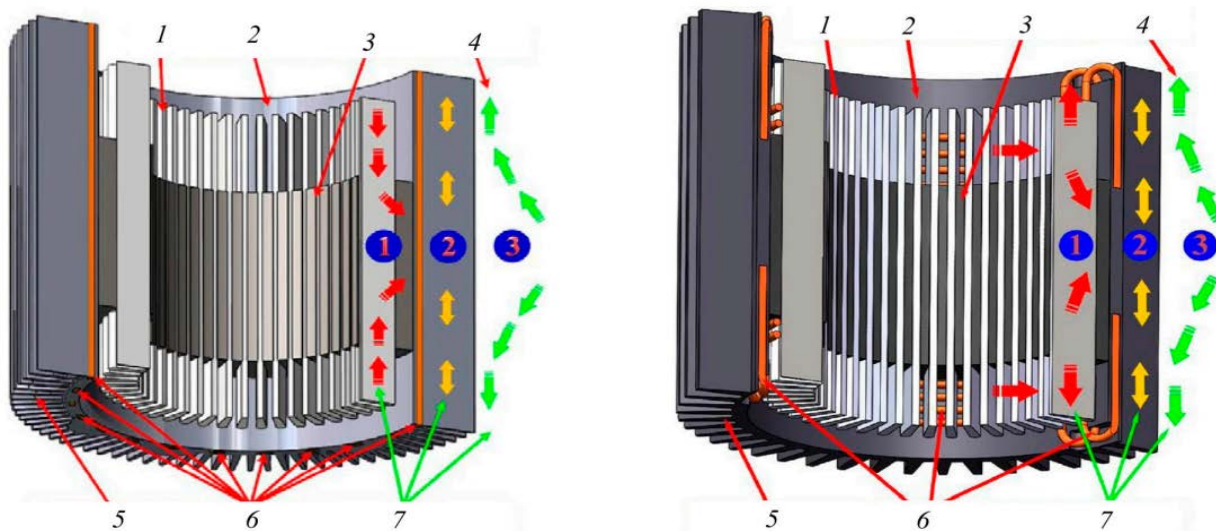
Охлаждение статора двигателя тепловыми трубами
